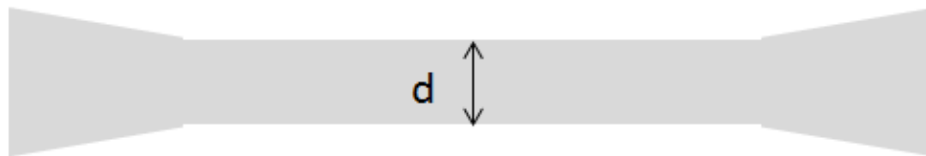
Camada de material que permaneceu no corpo de prova após usinagem
